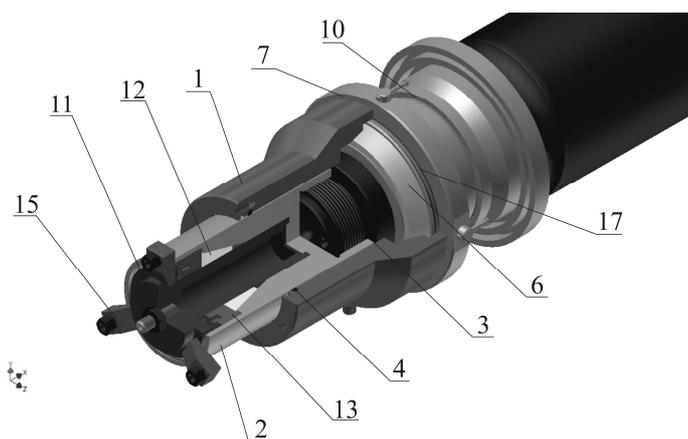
3D-модель конструкции устройства для гидрораспрессовки соединений с натягом колец подшипников с шейкой оси колесной пары
